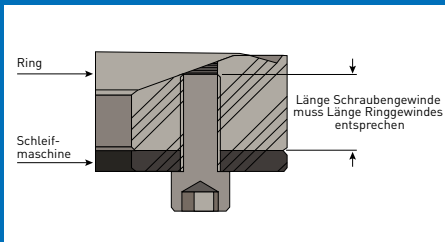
Die Schraubenlänge muss der Länge des Gewindes entsprechen
